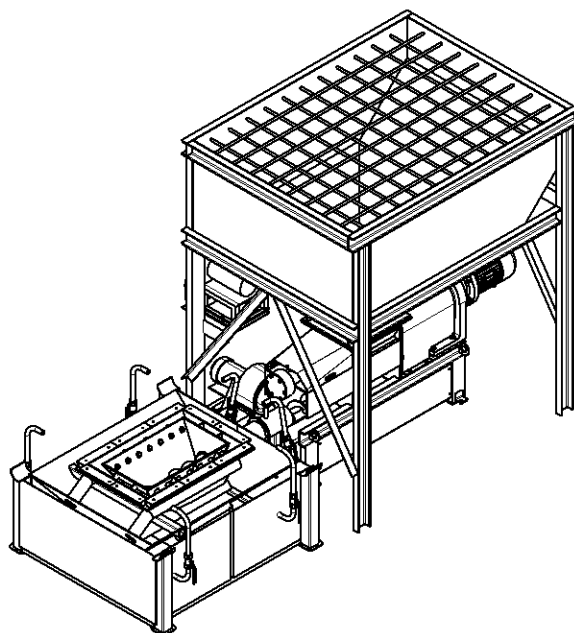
Общий вид ретортной топки. 3D-модель
